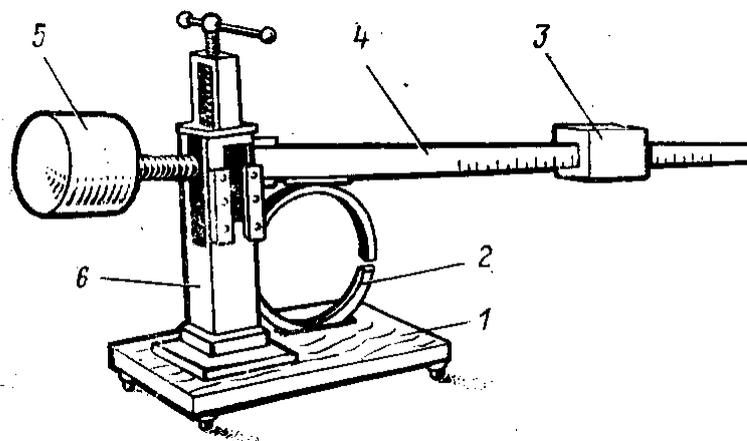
Рычажный прибор для проверки упругости поршневых колец: 1 – плита; 2 – поршневое кольцо; 3 – груз; 4 – рычаг; 5 – противовес; 6 – стойка
